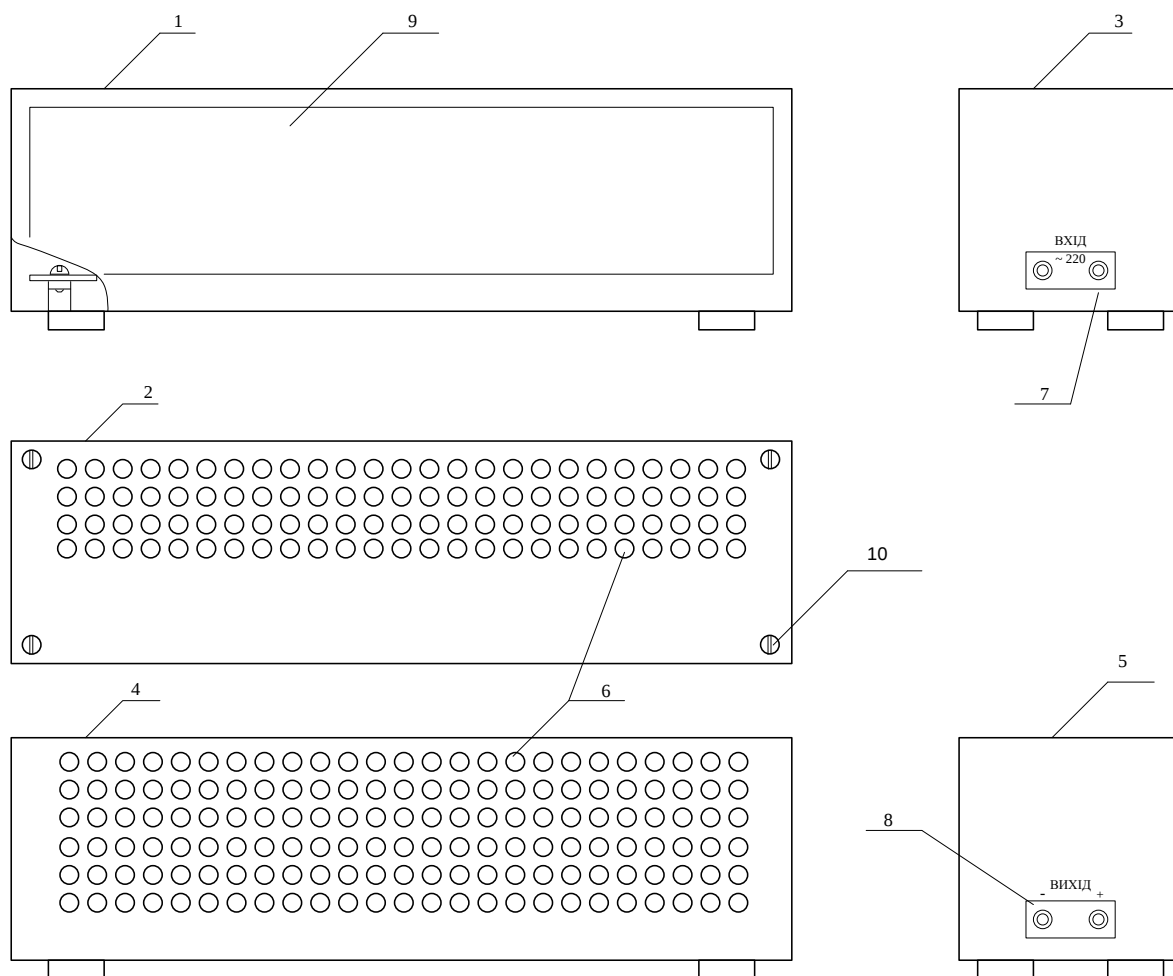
Перший і другий варіант компоновки конструкції корпусу
